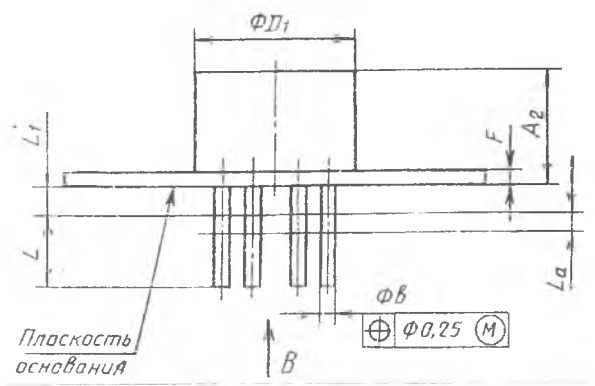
Конструкция корпуса типа 3 подтипа 2
